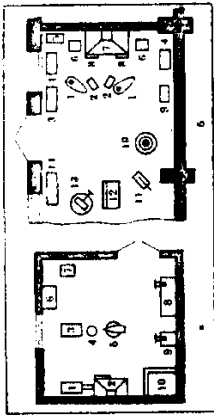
Размещение оборудования и инструментов в кузнице: а — кузница на одну наковальню (1 — вентилятор; 2 — горн; 3 — стол для инструмента; 4 — бачок с водой; 5 — наковальня; 6 — шкаф для инструментов; 7 — точило; 8 — верстак; 9 — кузнечные тиски; 10 — щипцы для углей); б — кузница на две наковальни (1 — наковальня; 2 — стол для инструмента; 3 — 4 — рабочие столы; 5 — шкаф; 6 — бачок с водой; 7 — горн; 8 — вешалки для клещей; 9 — точило; 10 — пневматический молот; 11 — ручные ножницы; 12 — правальная плита; 13 — ступовые тиски; 14 — столы для заготовок
